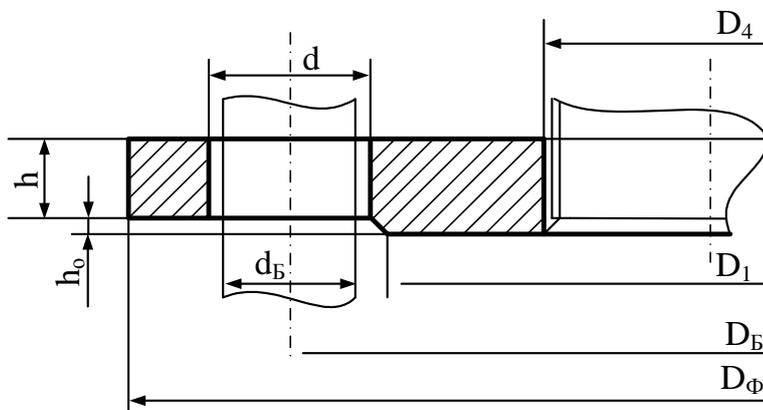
Типовая конструкция плоского приварного фланца для патрубков
